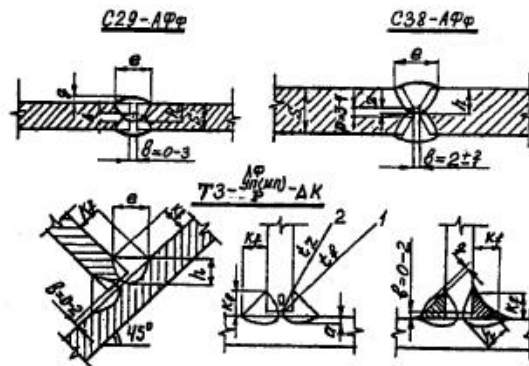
Геометрические параметры подготовки кромок и поперечного сечения шва.
